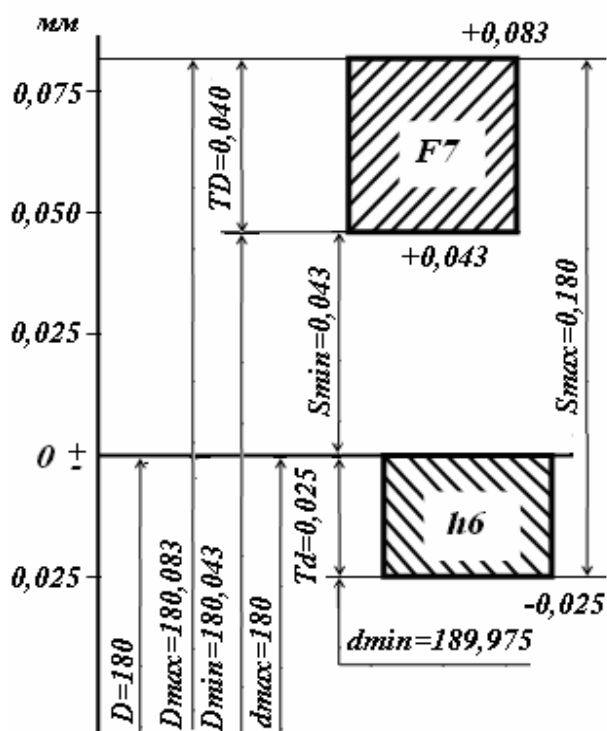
Схема розташування полів допусків з'єднання $\varnothing 180F7/h6$
